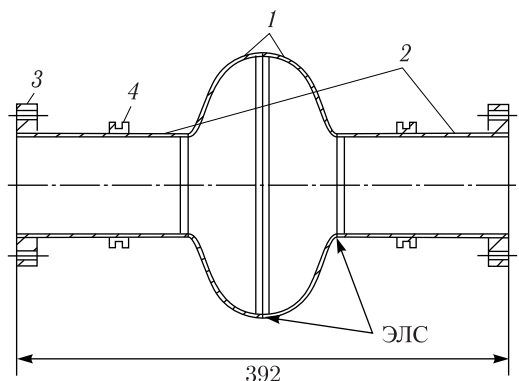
Одноячеечный резонатор 1,3 ГГц: 1 — полукамеры; 2 — трубки дрейфа; 3 — фланец; 4 — крепежный элемент. Показаны места электронно-лучевой сварки
